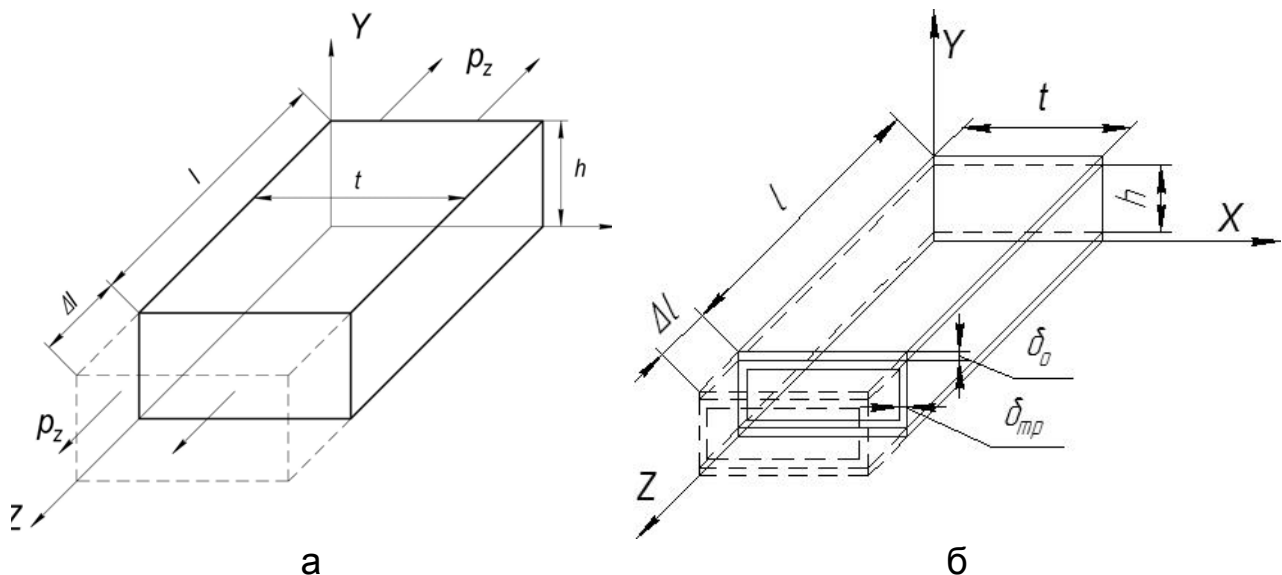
Типовой трубчатый элемент КМ с присоединенной обшивкой при нагружении вдоль оси Z: а – сплошной элемент; б – реальный трубчатый элемент с несущими обшивками
